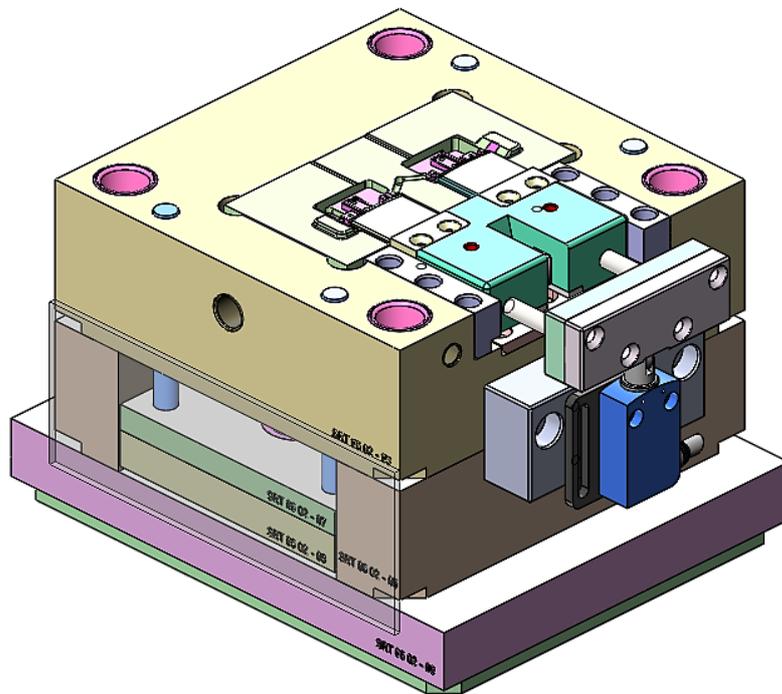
Bucha do molde que sobreinjeta a peça com SEBS.
